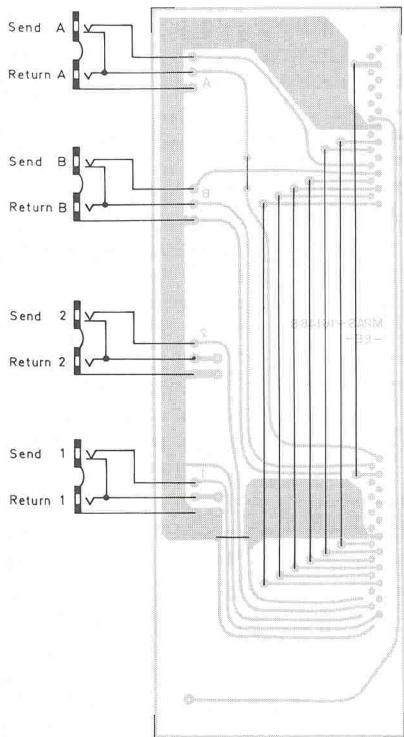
Die ECB-Platine wird nur mit einigen Drahtbrücken bestückt.
